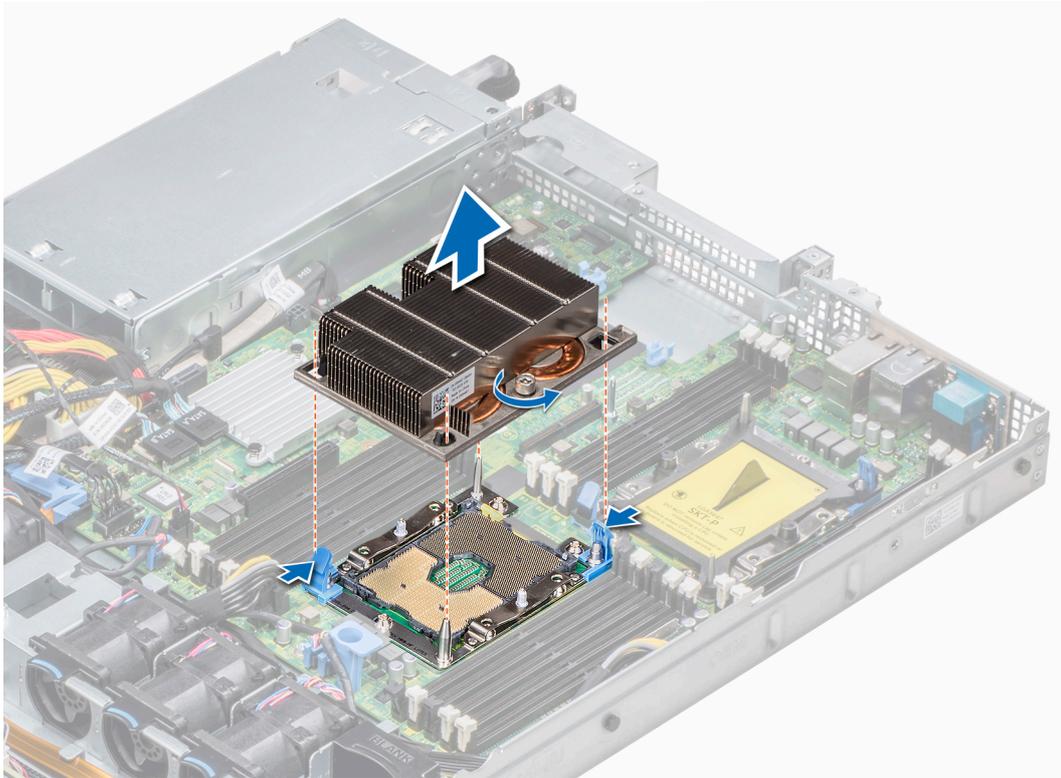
Entfernen des Prozessor- und Kühlkörpermoduls
